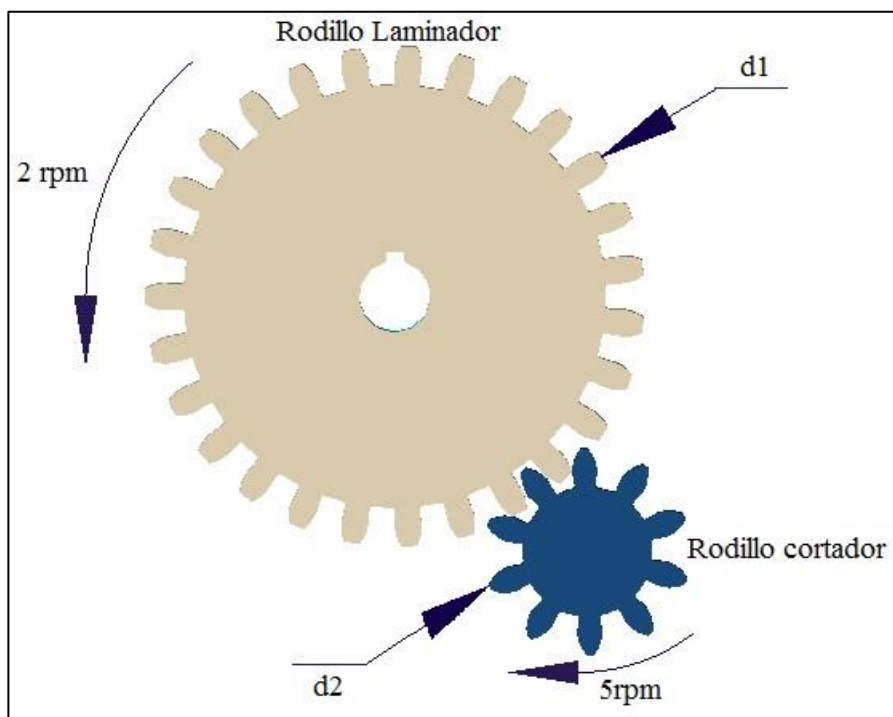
Transmisión entre rodillo laminador y cortador (Fuente propia).
